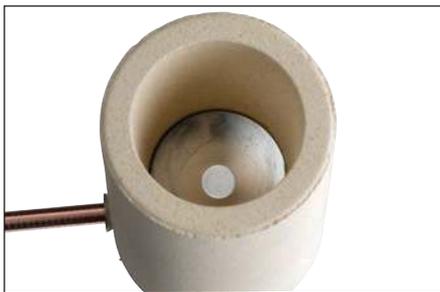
Assurez-vous que le disque d'acier est correctement installé à l'intérieur du Cadweld One Shot.
